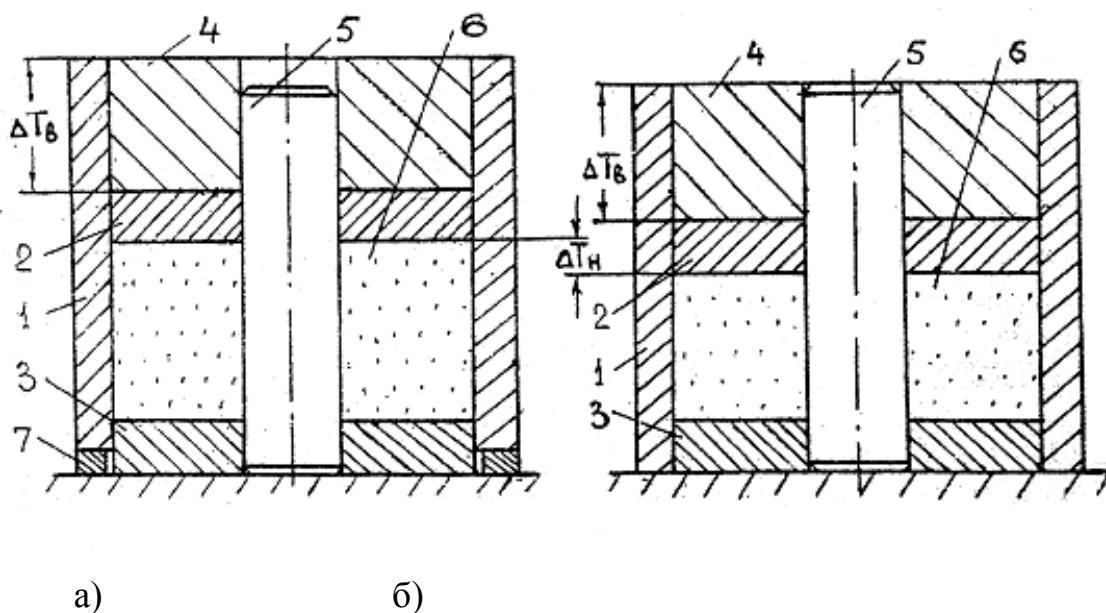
Схема одностороннего прессования с подвижной матрицей и подпрессовкой:
